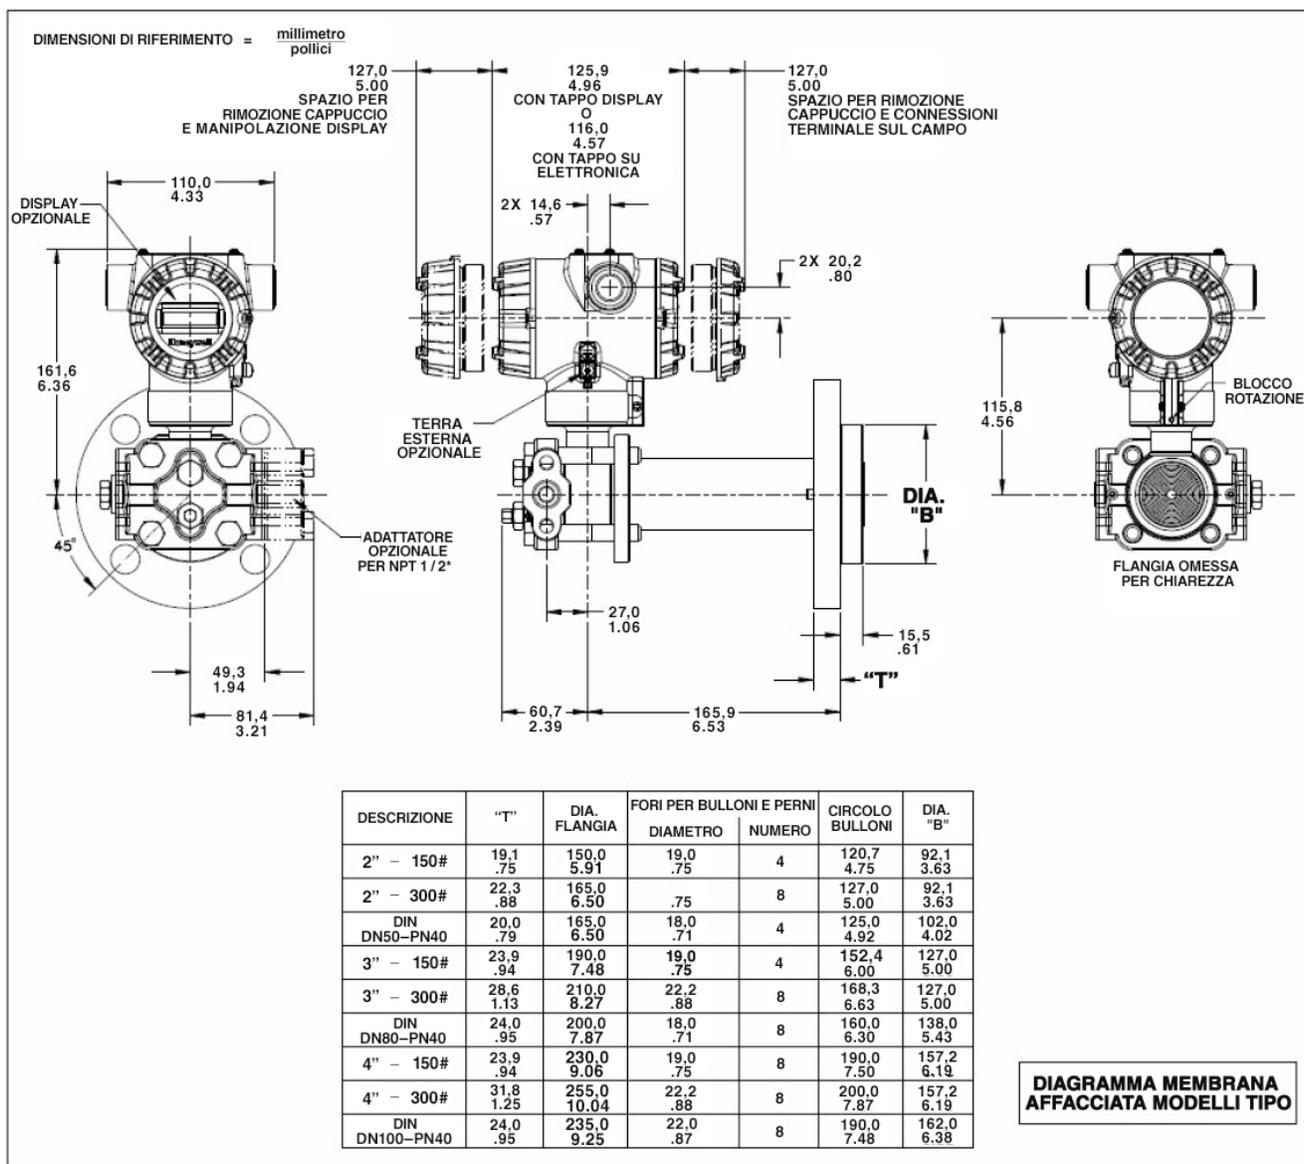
Dimensioni di montaggio tipiche per i modelli con membrana affacciata STF828 e STF832.
